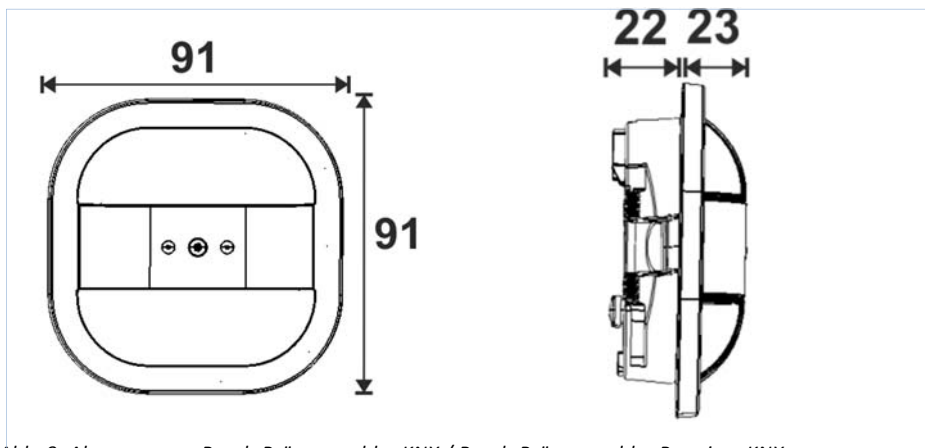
Abmessungen Busch-Präsenzmelder KNX / Busch-Präsenzmelder Premium KNX
